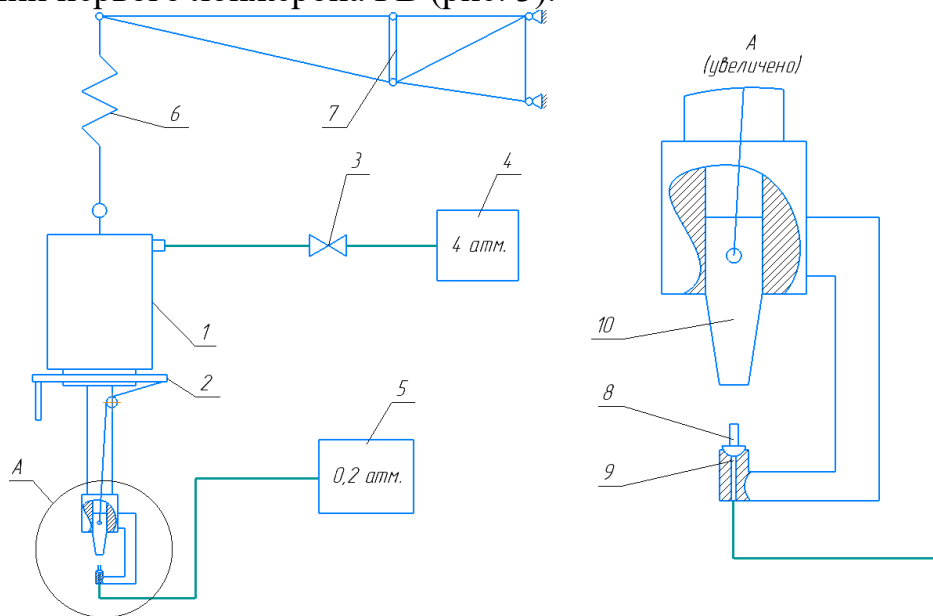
Схема пневмо-вакуумного пресс-заклепочника: 1 – пневмо-вакуумный пресс-заклепочник; 2 – спусковой механизм; 3 – педаль; 4 – компрессор; 5 – вакуумный насос; 6 – пружина; 7 – балка; 8 – заклепка; 9 – нижний боек с полостью; 10 – верхний боек
